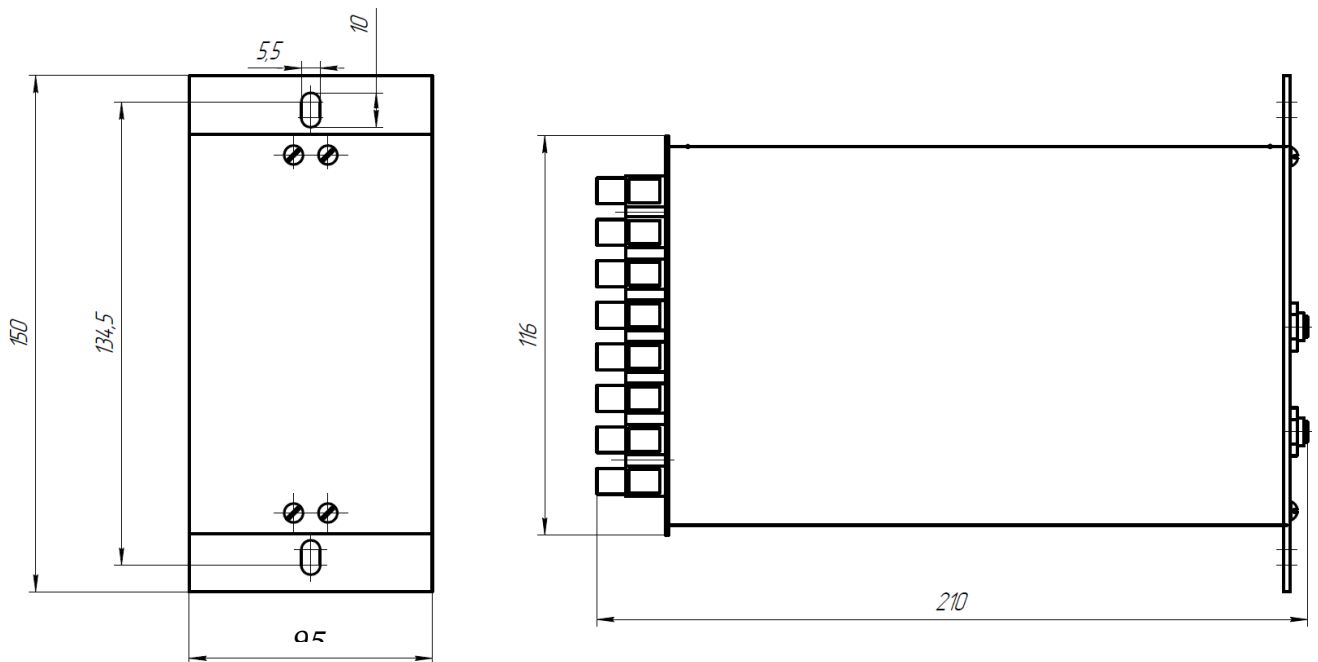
Габаритные размеры реле РДЗ-012МТЗ.3
